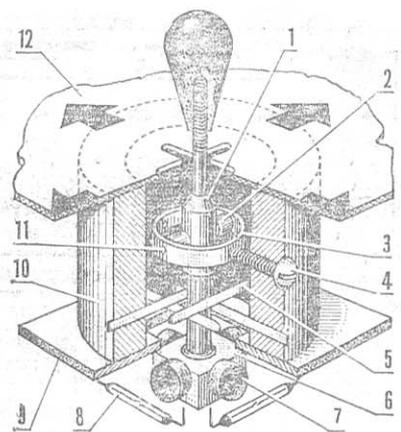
Механизм подачи команд: 1 — рукоятка управления, 2 — втулка, 3 — кольцо, 4 — винт М3, 5 — стальная пружина, 6 — магнитодержатель, 7 — магнит, 8 — геркон, 9 — пластина, 10 — цилиндрический корпус, 11 — шпилька, 12 — корпус передатчика.
